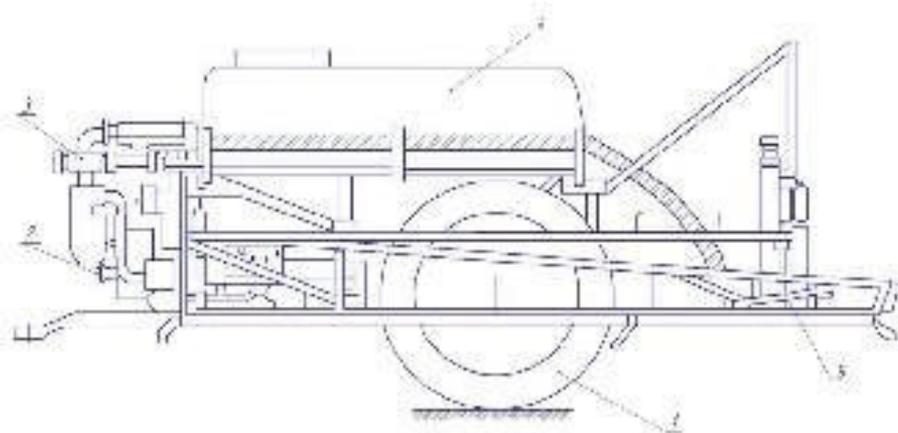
Штанговый опрыскиватель ОП-2000
